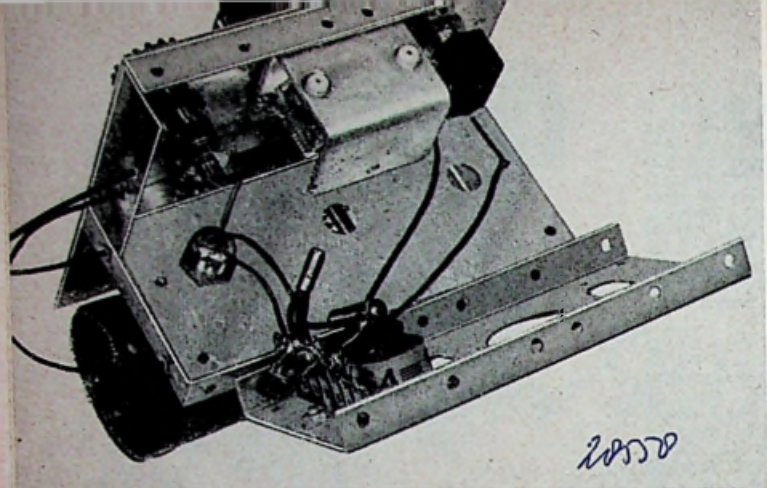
MONTAGEPLAN VAN DE UN-85
